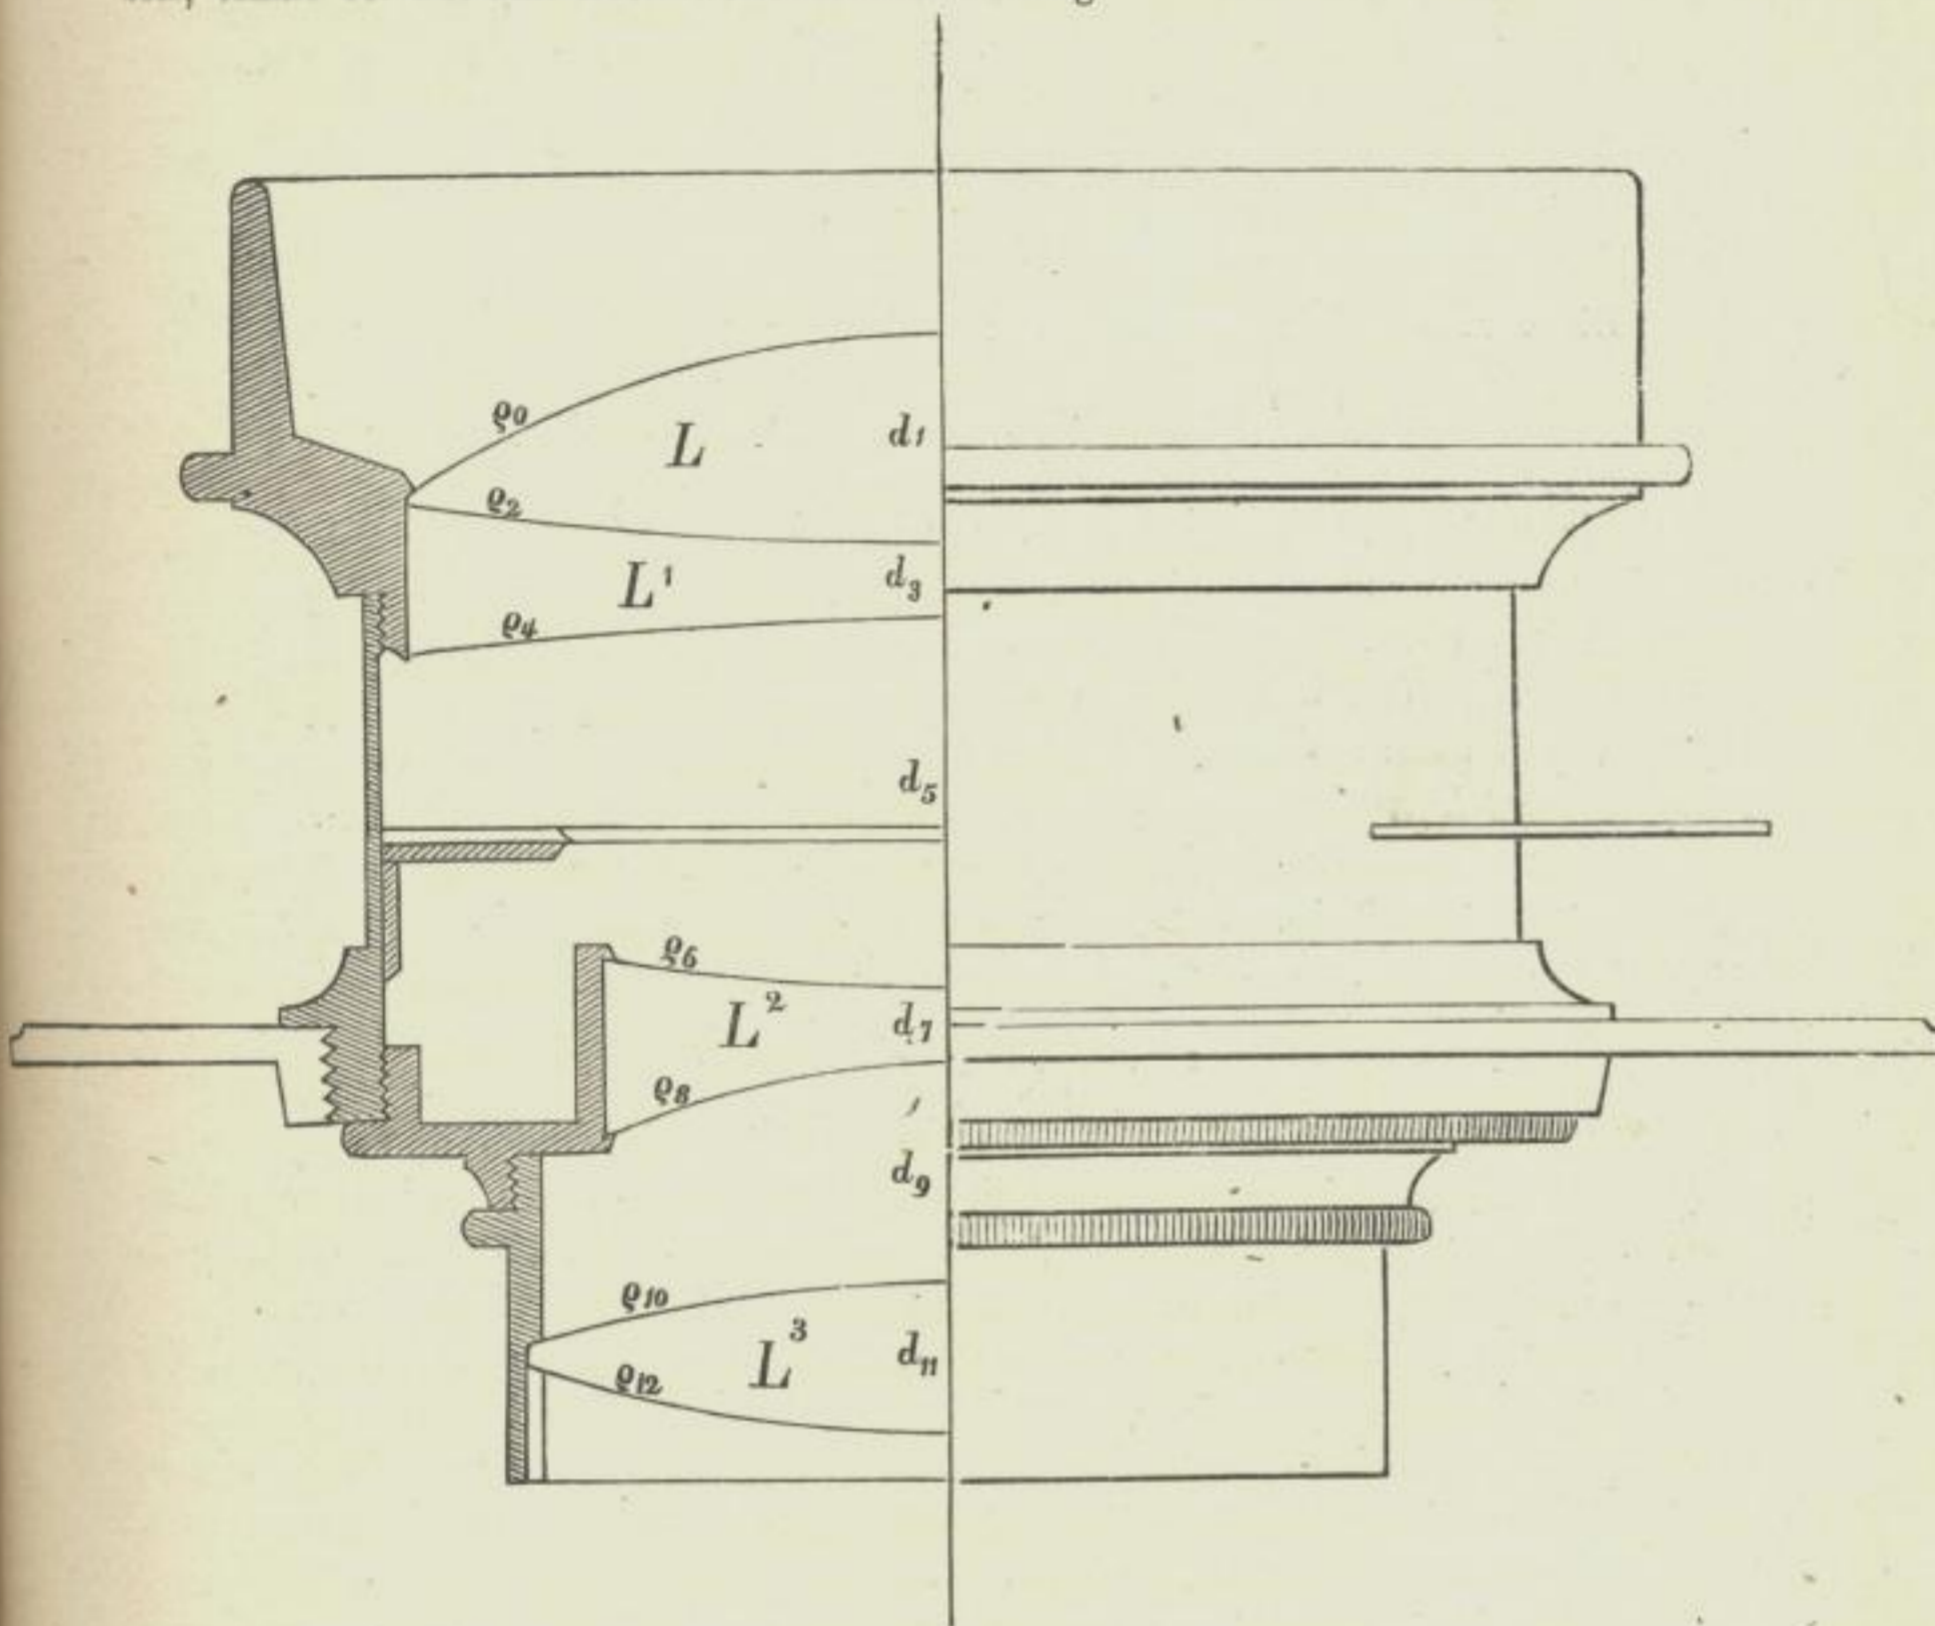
Steinheils Antiplanet für Porträte. $f = 240$ mm.
